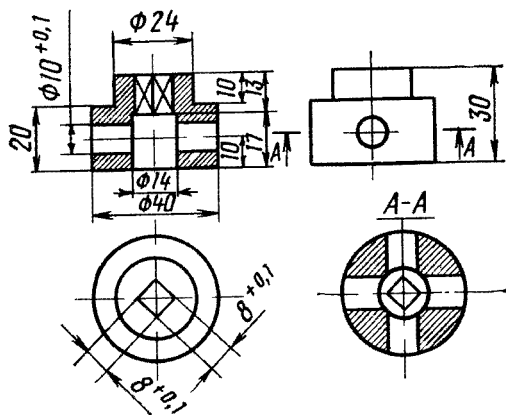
Приспособление для снятия ступицы заднего колеса:
